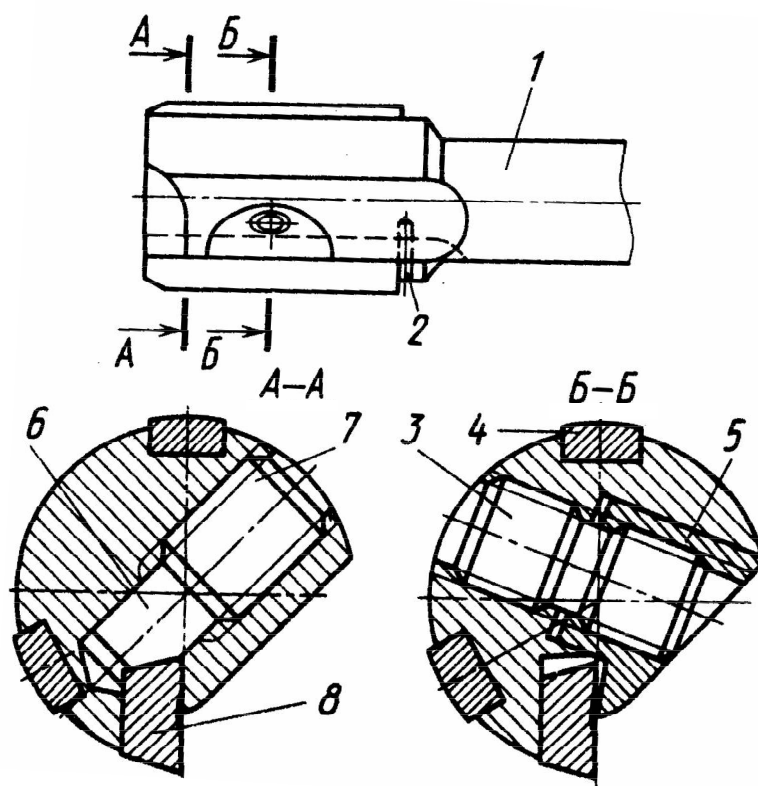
Однолезова розвертка „Мапал”: 1 – корпус; 2 – упорний штифт; 3 – кріпильний гвинт; 4 – твердосплавна планка; 5 – притискач; 6 – сухар; 7 – регулювальний гвинт; 8 – твердосплавна різальна пластина
